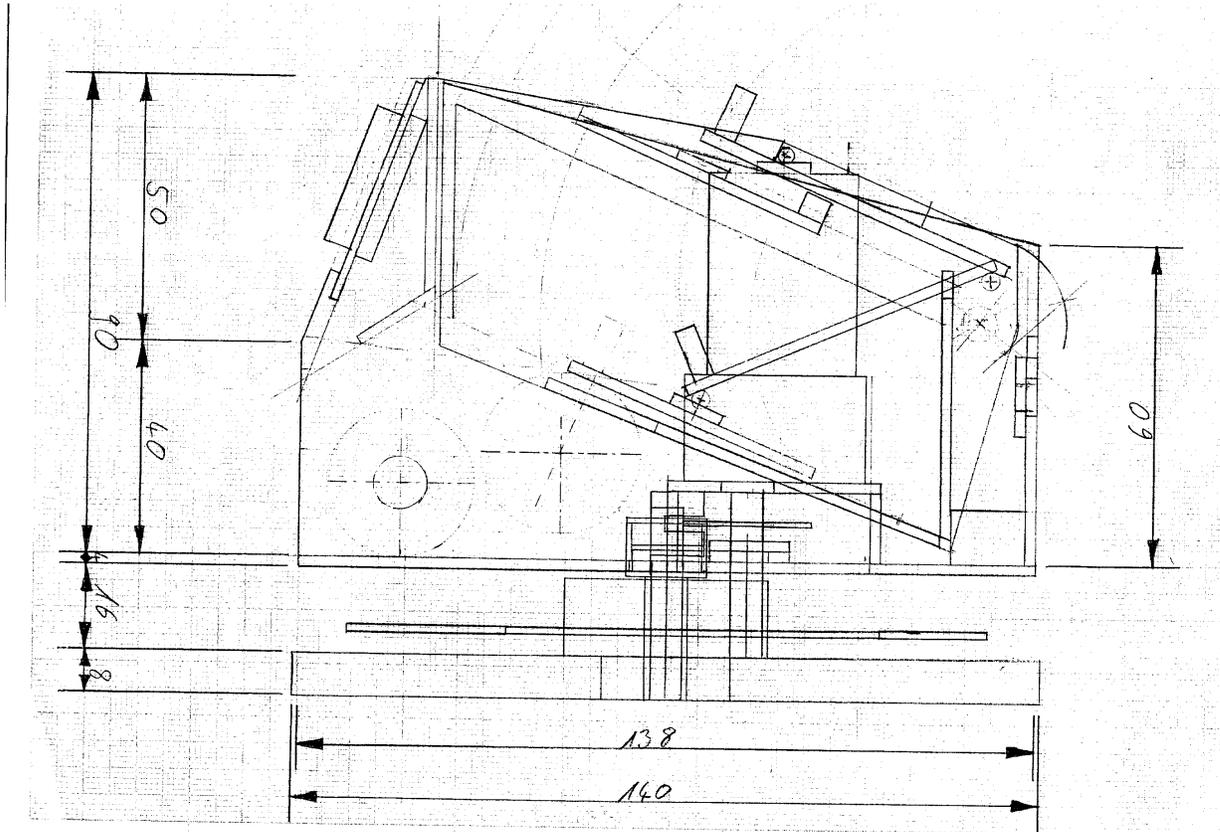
Zeichnung Seitenansicht Kartenausteil
